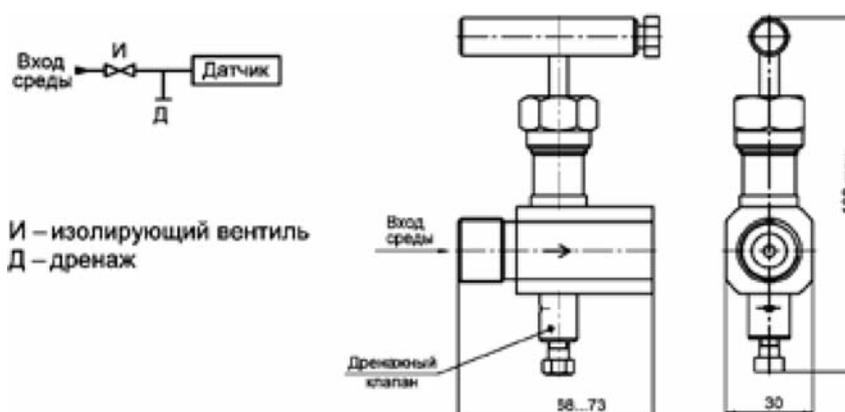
Схема и габаритные размеры одновентильного блока ВБ1.
